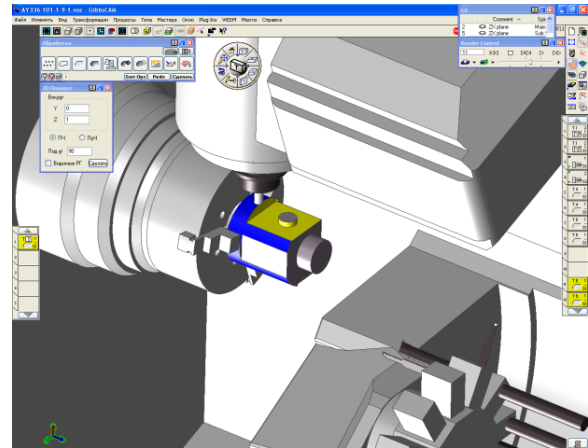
Выполнение обработки фрезерным мотор – шпинделем
